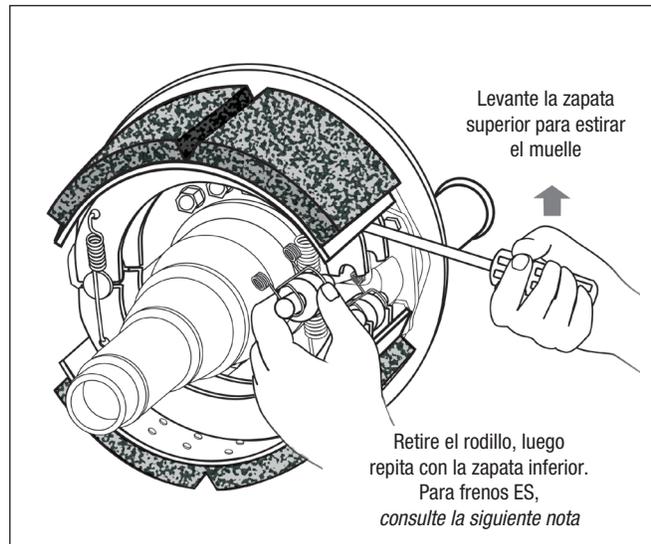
Desmontaje del pasador y el rodillo de leva superior
